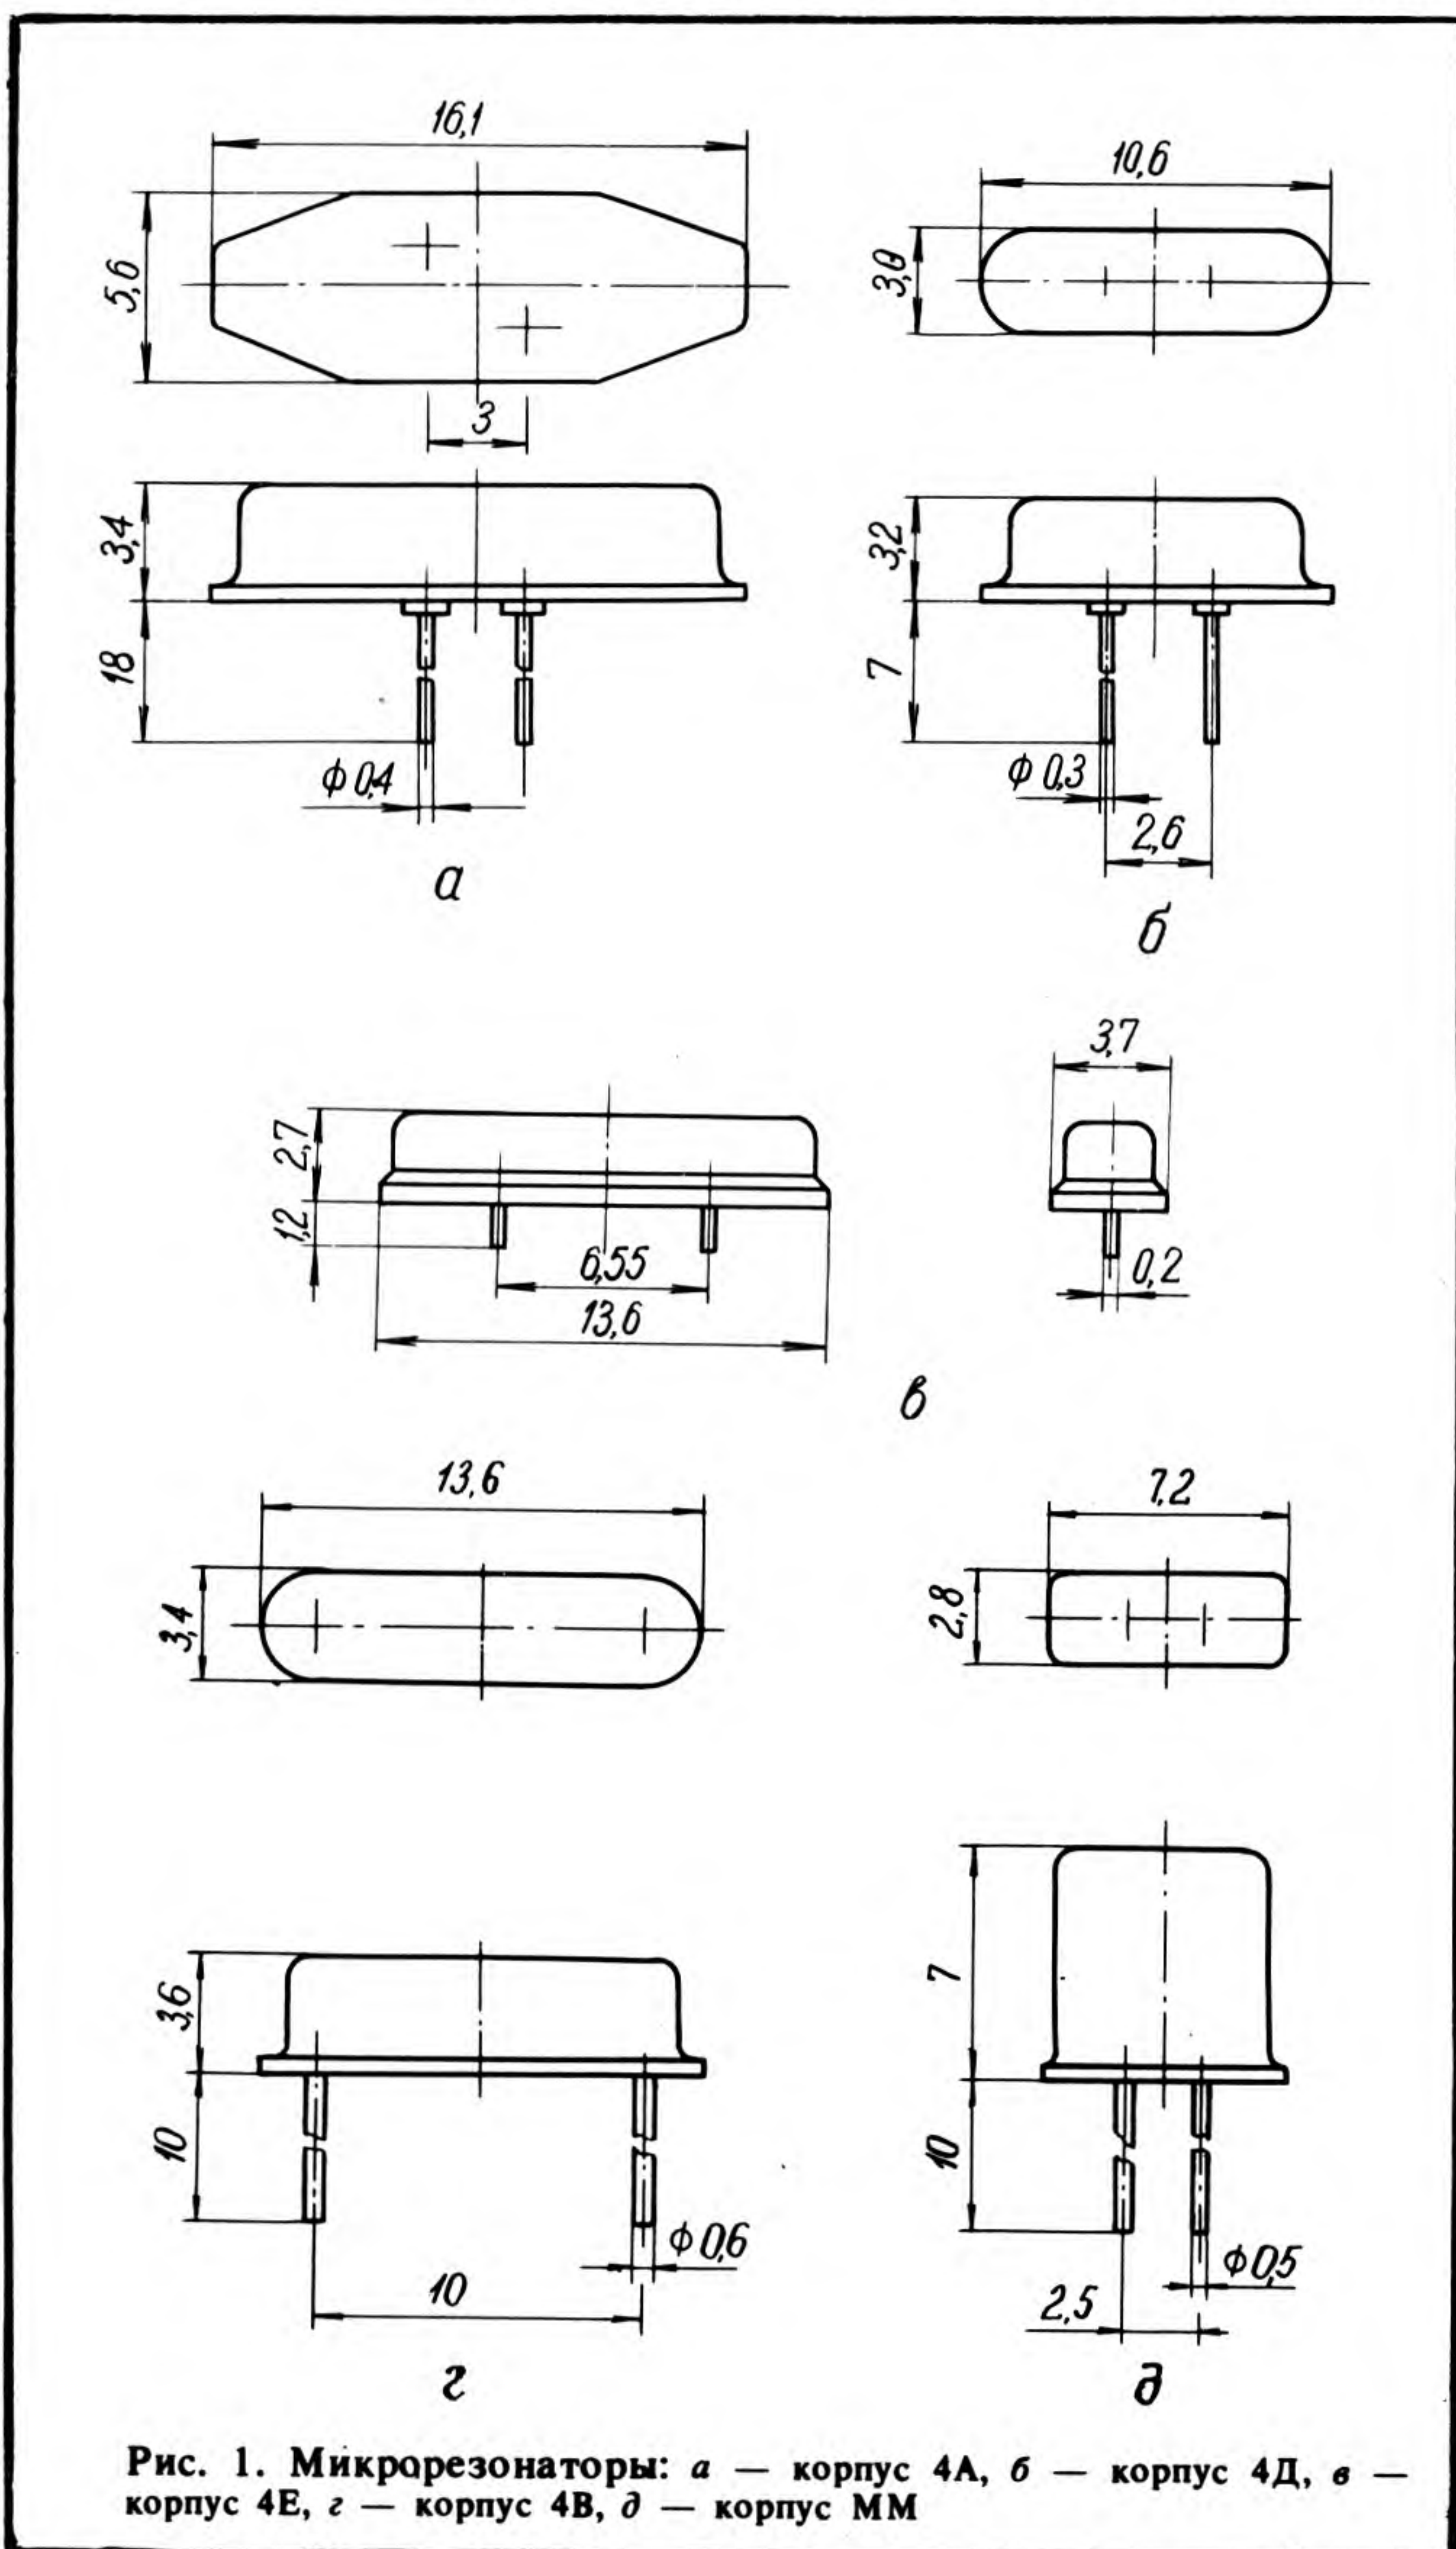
Микрорезонаторы: а — корпус 4А, б — корпус 4Д, в — корпус 4Е, г — корпус 4В, д — корпус ММ
